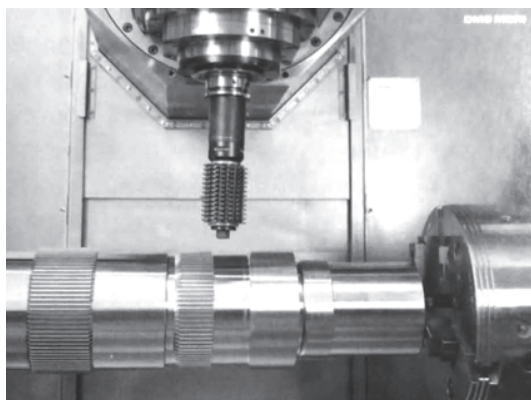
Метод зубообработки GEARHOBGING на станке DMGMORI
